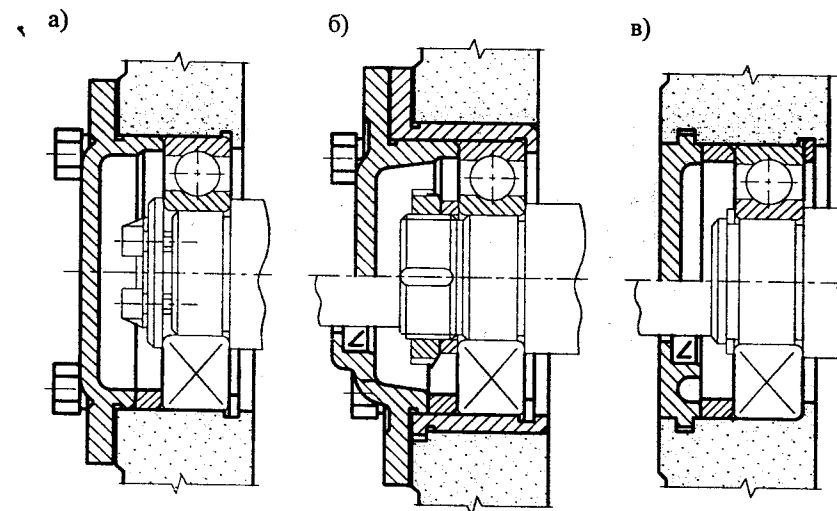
Установка наружного кольца неразъемного подшипника в корпусе фиксирующей опоры
